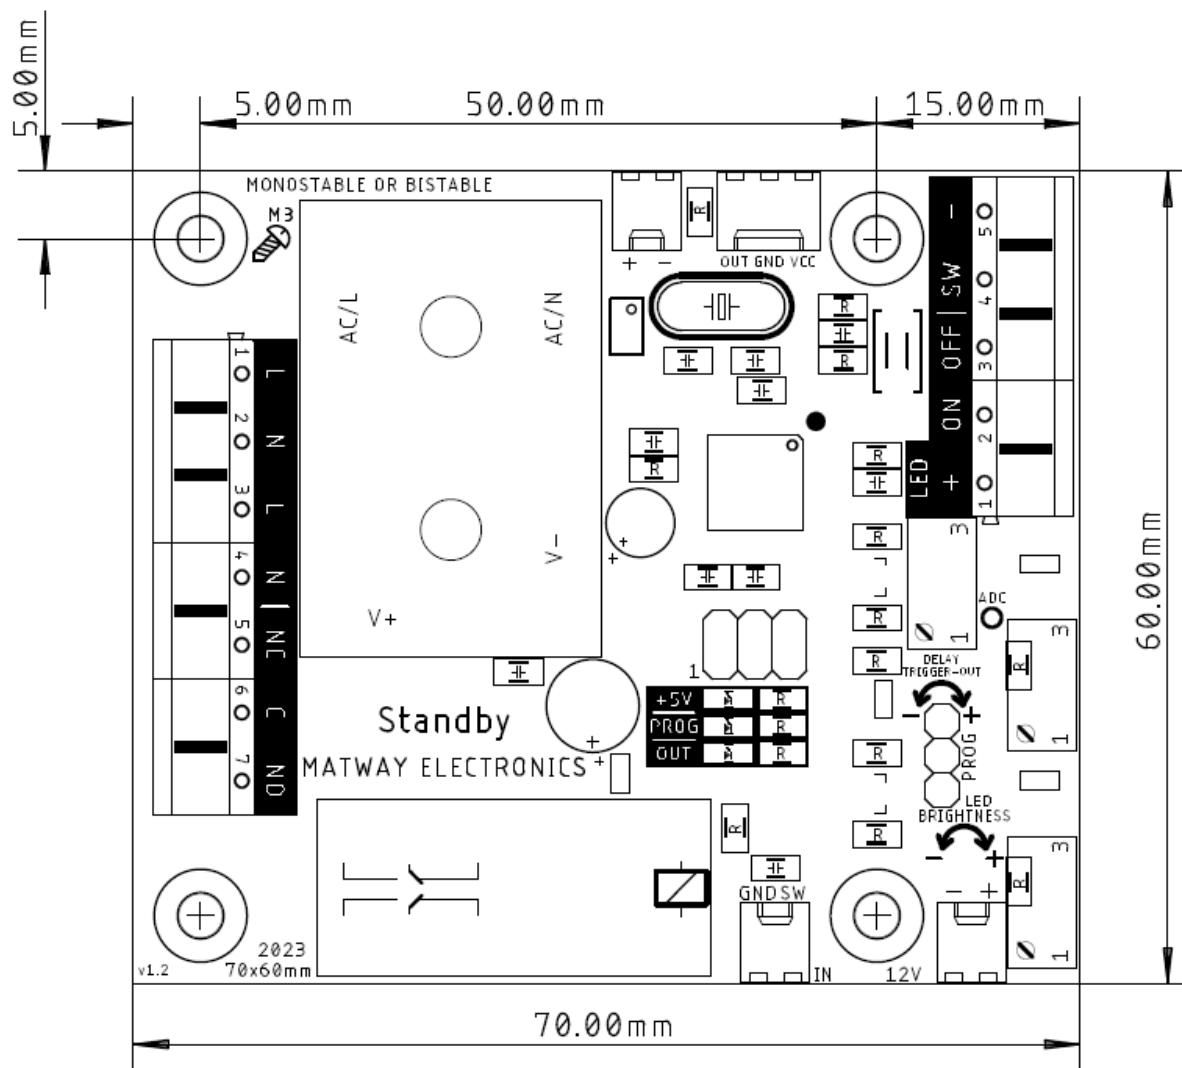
Podgląd PCB v1.2 – BOTTOM
